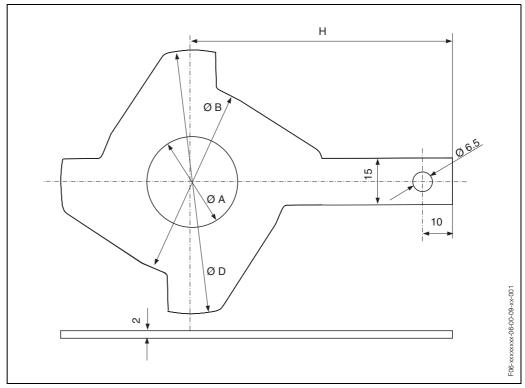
Dimensions disque de masse (Promag P / DN 25...200)
